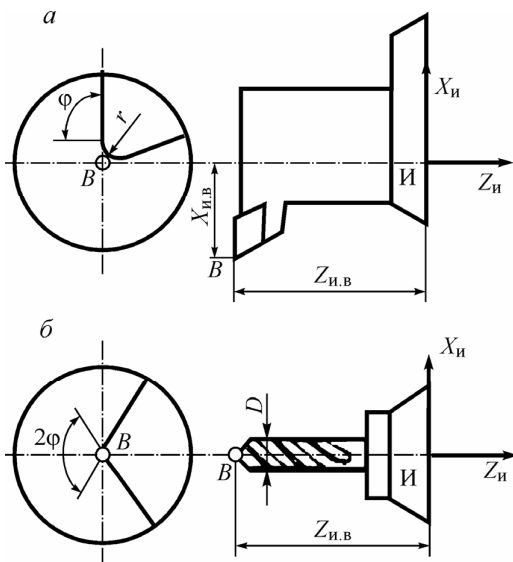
Схема координат инструмента при обработке на токарном станке
